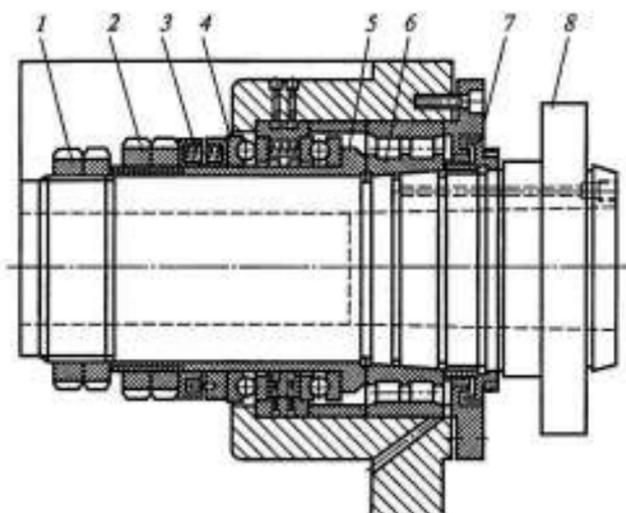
Передняя опора шпинделя токарного станка на подшипниках качения:
